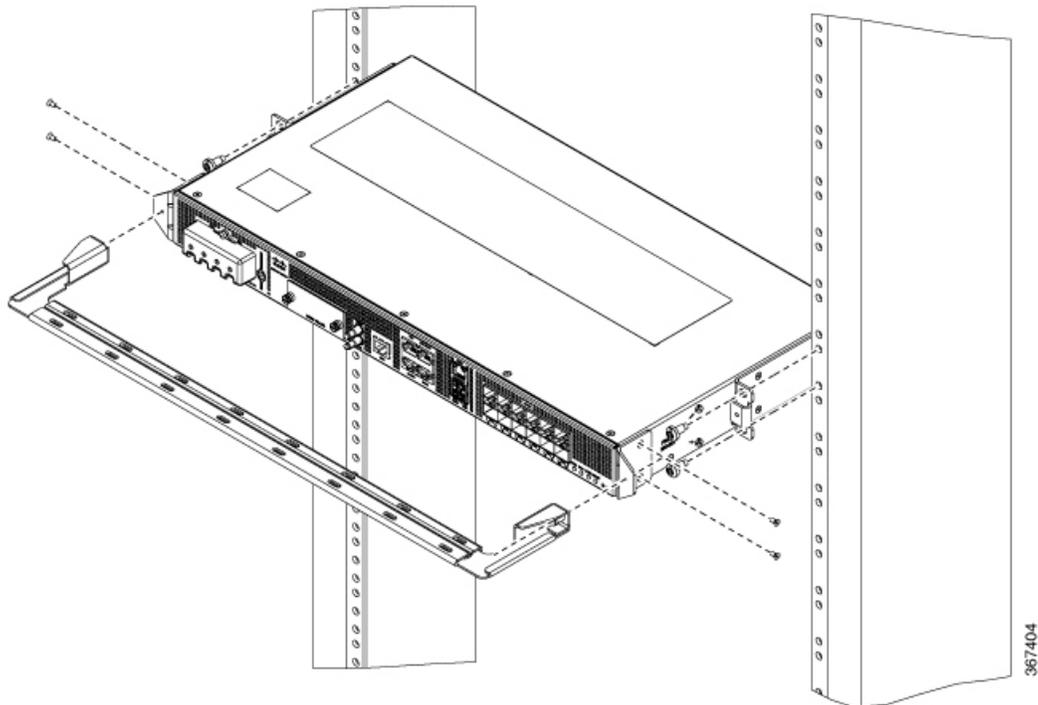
Dispositif de fixation arrière avec guide-câble sur un rack de 19 pouces
